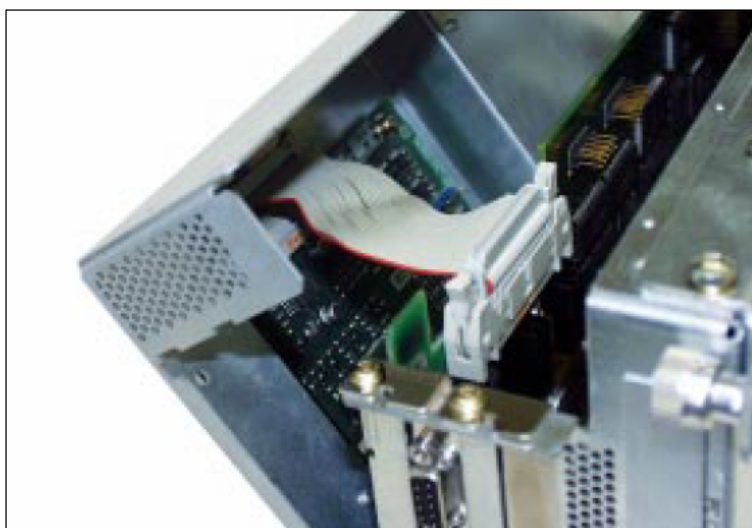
Измененная крышка корпуса с MCI-Board-Extension внешний вариант
